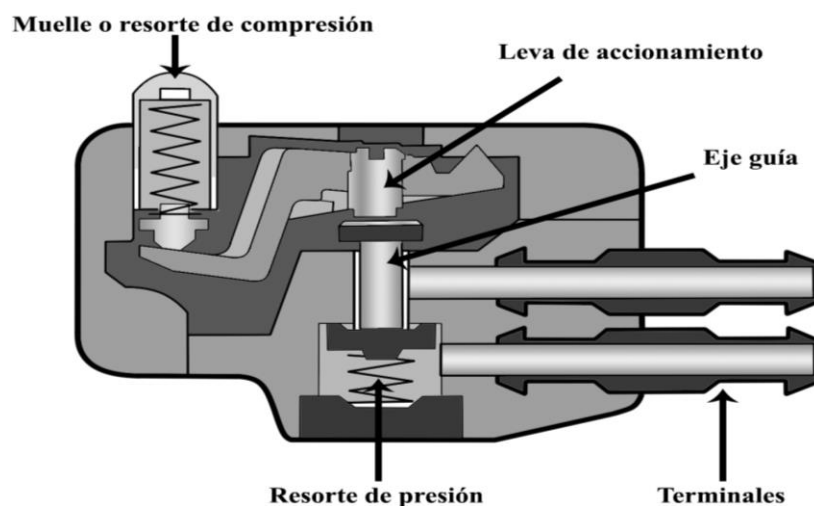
Estructura interna de un final de carrera mecánico-neumático.
